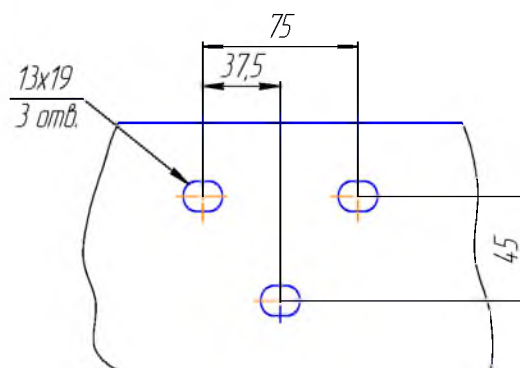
Разметка крепёжных отверстий для установки привода
